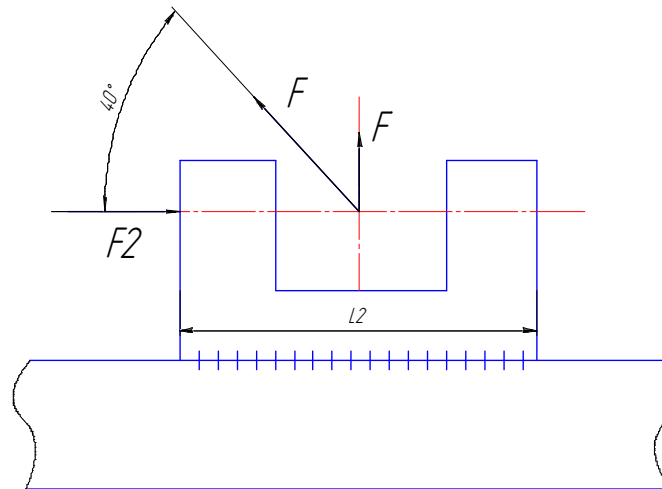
Розрахункова схема зварного шва кронштейна гідроциліндра колісного ходу
